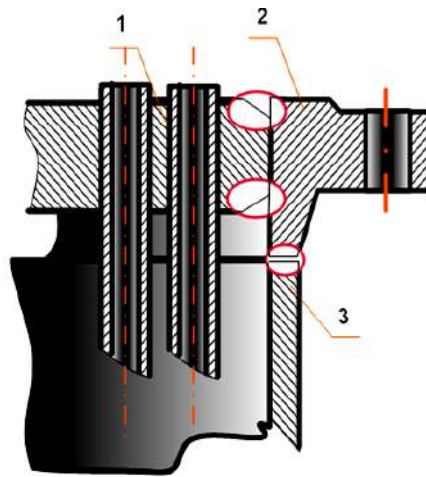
Фланцевый корпус с бесфланцевой решеткой
